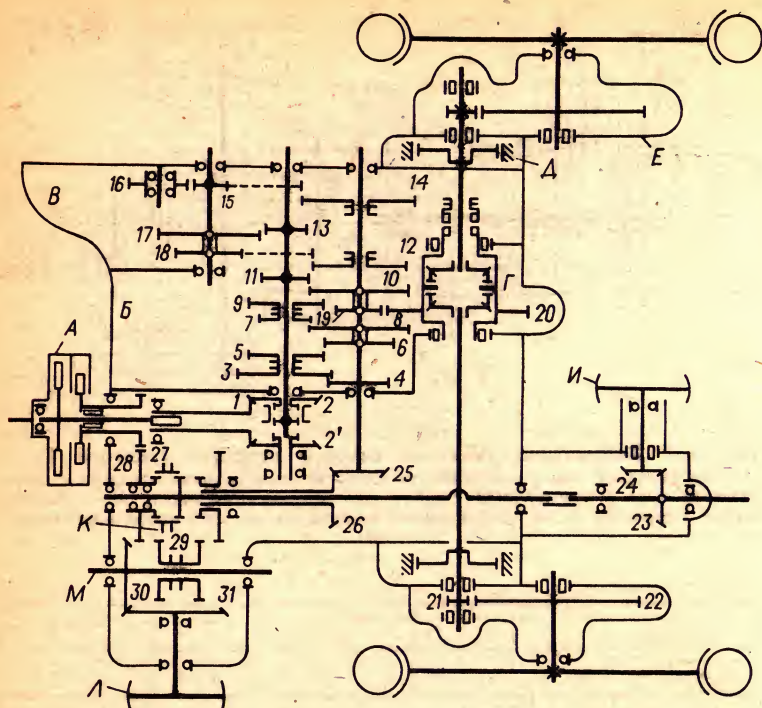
Кинематическая схема силовой передачи трактора Т-40: А — двухпоточная муфта сцепления; Б — коробка передач; В — ходоуменьшитель; Г — центральная передача с дифференциалом; Д — ленточный тормоз; Е — конечная передача; И — задний приводной шкив к ВОМ; К — зубчатая муфта переключения ВОМ на независимый или синхронный привод; Л — боковой шкив; М — боковой вал отбора мощности
